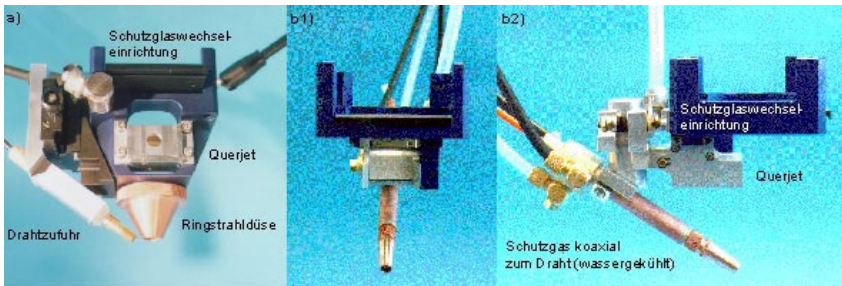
Bearbeitungsköpfe zum Laserstrahlschweißen mit integrierter Schutzglaswechseleinrichtung und Querjet für  $f = 100 \text{ mm}$ : a) modulare, gekapselte Lösung mit Ringstrahldüse zur Schutzgaszufuhr, b) offene, bauraumoptimierte Lösung mit wassergekühlter Schutzgaszuführung koaxial zur Drahtzufuhr (11 mm Außendurchmesser); b1) Ansicht in Schweißrichtung, b2) senkrecht dazu.
